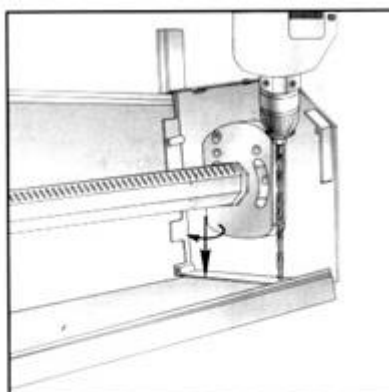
Сверление отверстий в верхней отбортовке крышки при встроенном монтаже.
